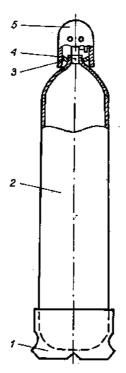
Водородный баллон. 1- опорный башмак; 2- корпус; 3- кольцо горловины; 4- вентиль; 5- предохранительный башмак.
